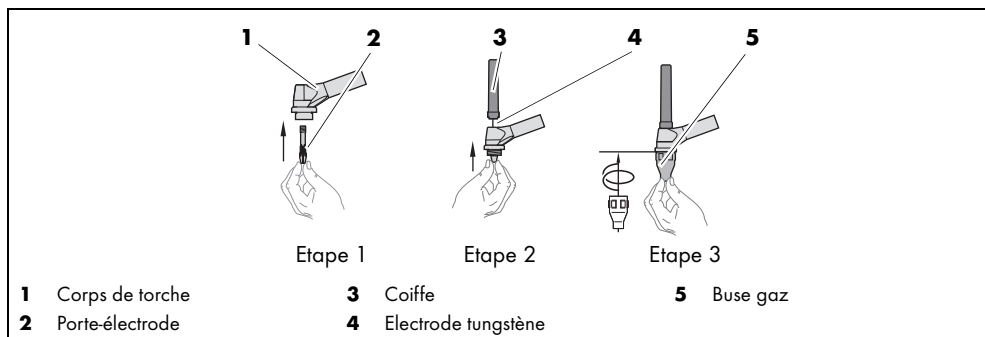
Torche de soudage ABITIG® Little 150, 260W
